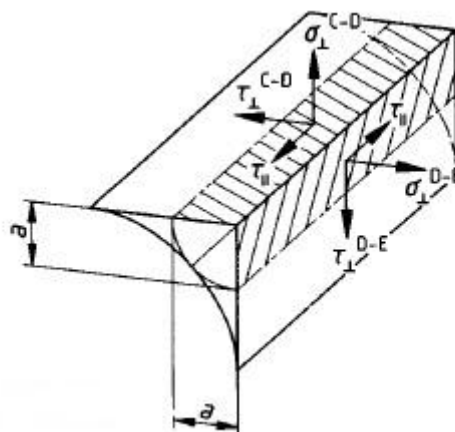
Schweißnahtspannungen Kehlnaht⁵⁸
